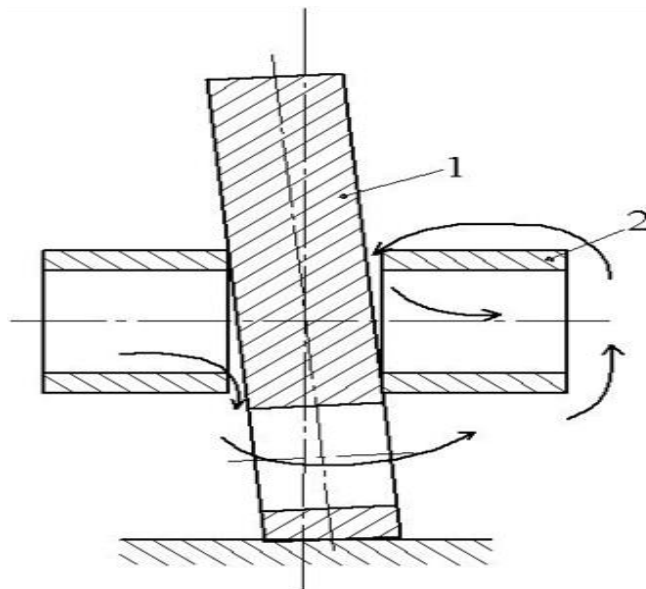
Шибер затиснутий між шпинделем і корпусом засувки
